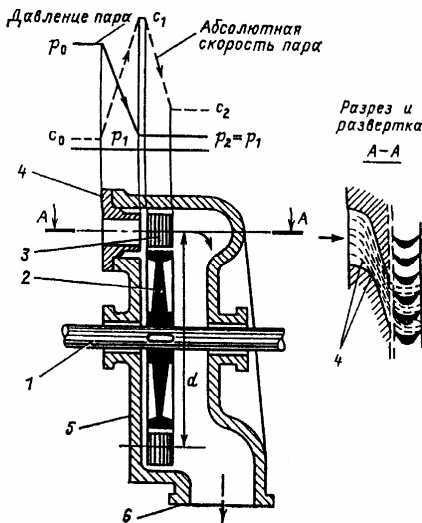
Схематический разрез одноступенчатой активной турбины: 1 – вал; 2 – диск; 3 – рабочие лопатки; 4 – сопловая решетка; 5 – корпус; 6 – выпускной патрубок
